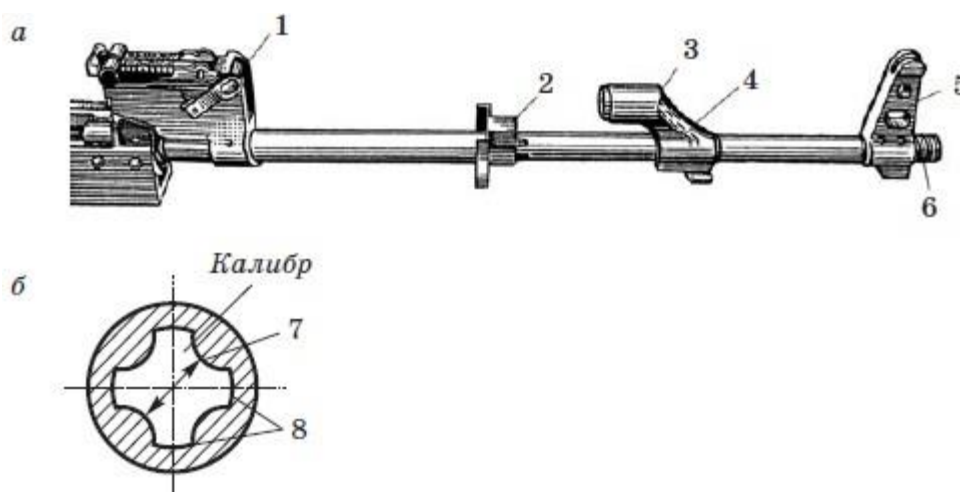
Ствол: а — общий вид; б — сечение ствола; 1 — колодка прицела; 2 — соединительная муфта; 3 — газовая камера; 4 — газоотводящее отверстие; 5 — основание мушки; 6 — резьба; 7 — поле; 8 — нарезы
